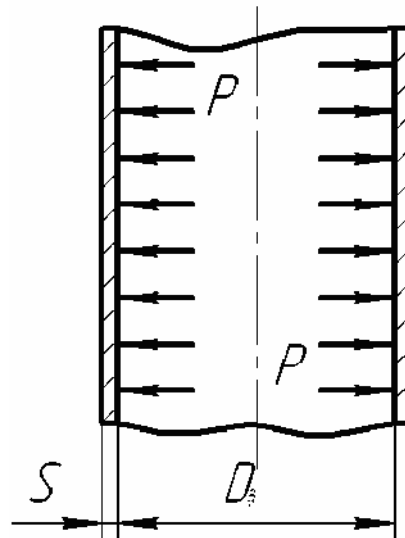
Розрахункова схема циліндричної обичайки
